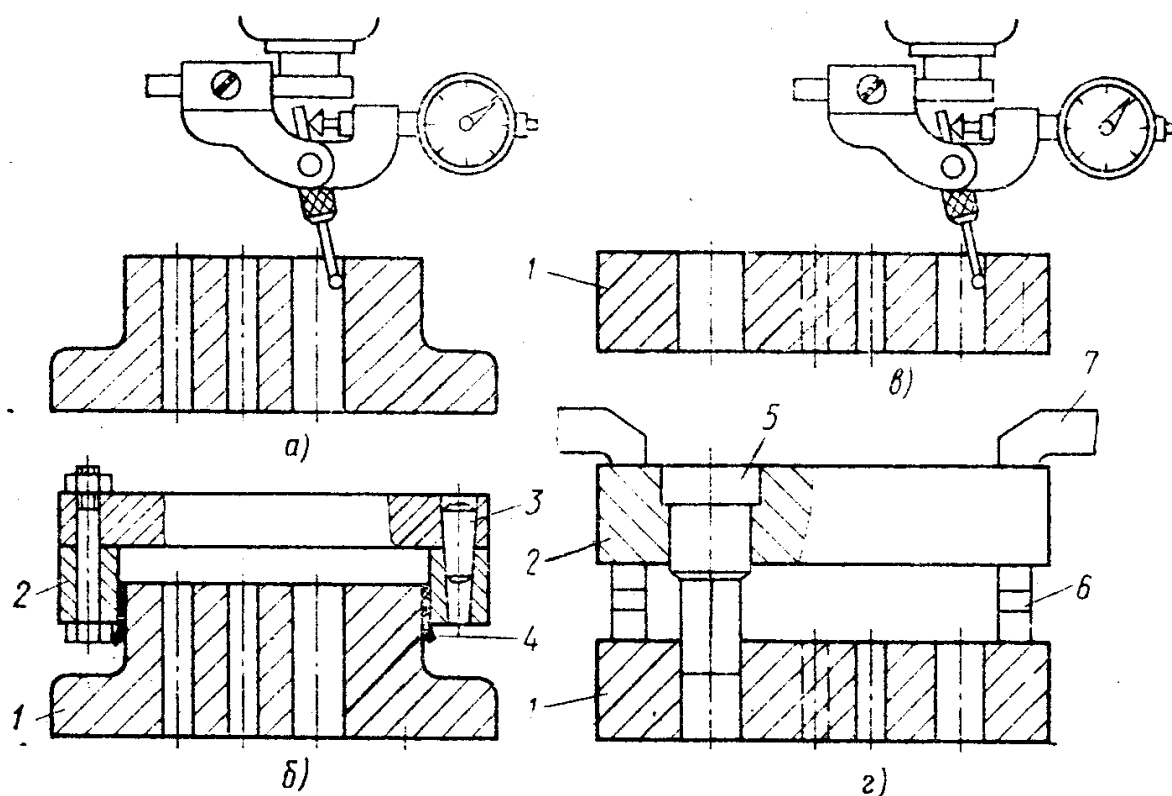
Схема переноса координат отверстий матриц или пуансоно-матриц на пуансонодержатель с помощью координатно-расточного станка
